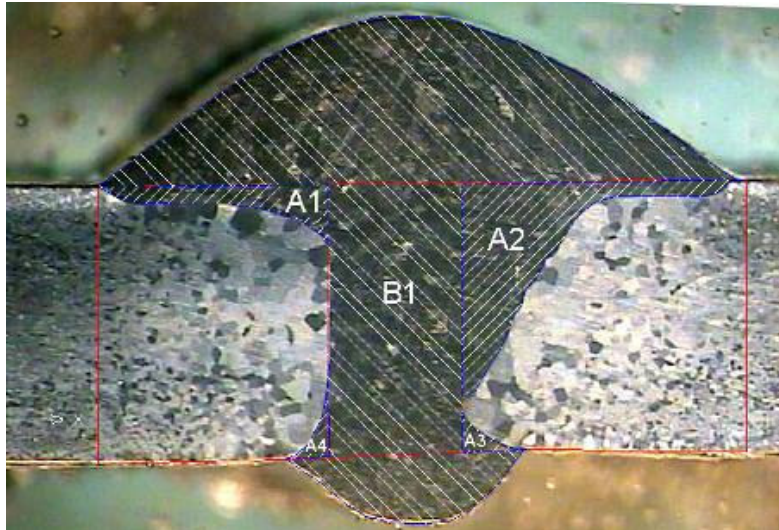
Junta soldada do aço AISI 444 soldado com o consumível AISI 316LSi; destaque para as áreas demarcadas para o procedimento de cálculo da diluição; reativo: Villela; aumento: 10X.
